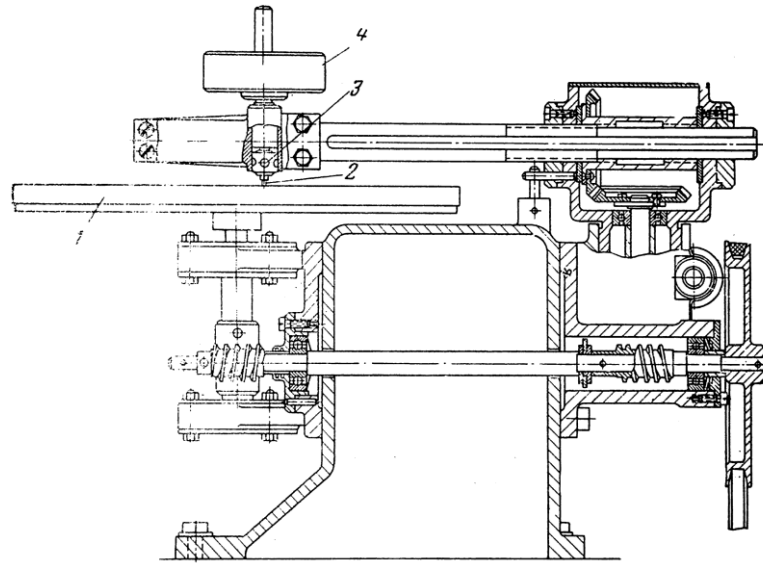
Схема машини Х4-Б [7]: 1 – диск; 2 – зразок; 3 – державка; 4 – вантаж.
